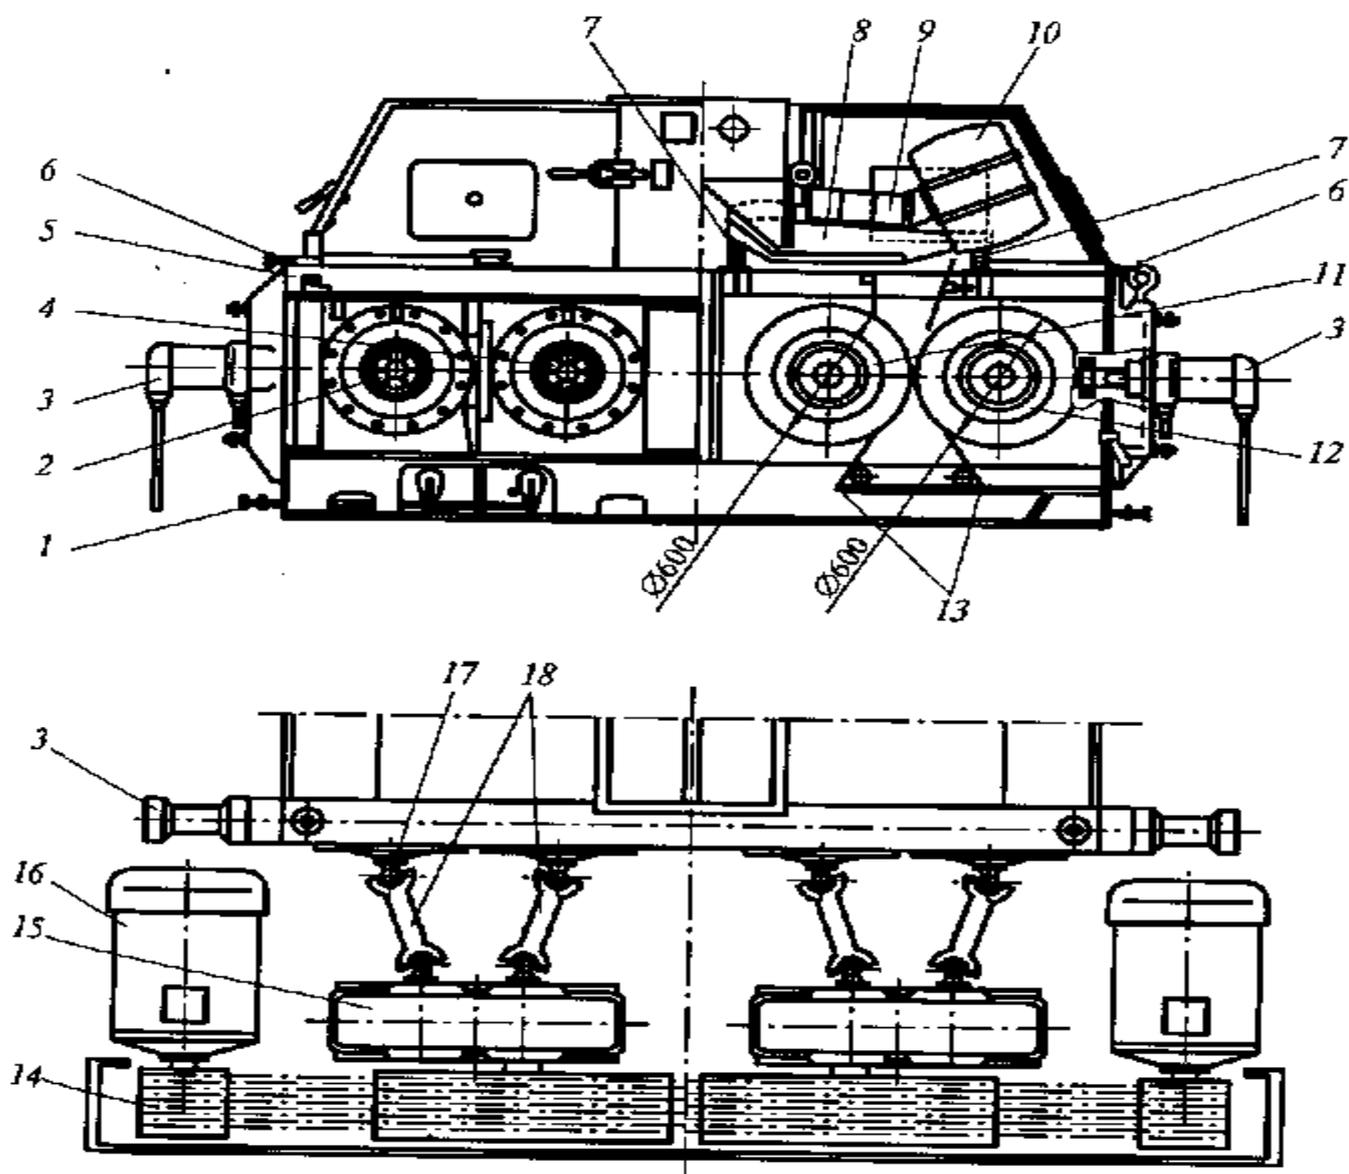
Двухпарный плющильный вальцовый станок ФВ-600
